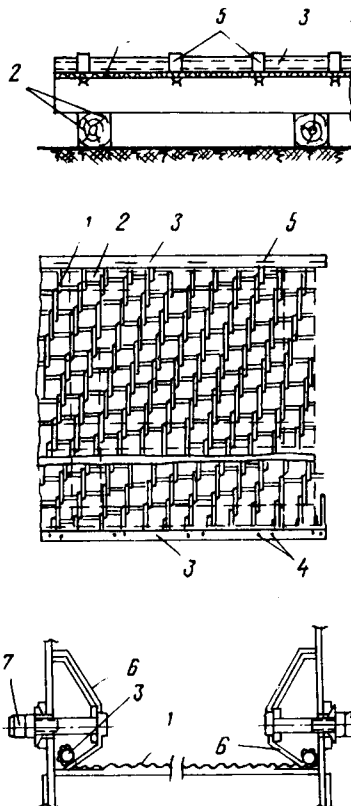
Схема крепления и поперечного натяжения плетеного сита на виброгрохоте ГУП-II:
